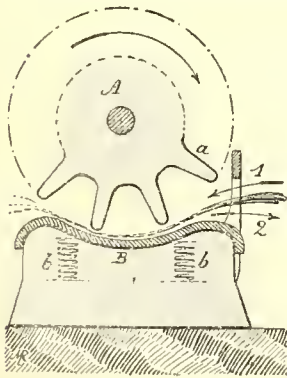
Machine à china-grass (Lacôte et Marcou frères).
